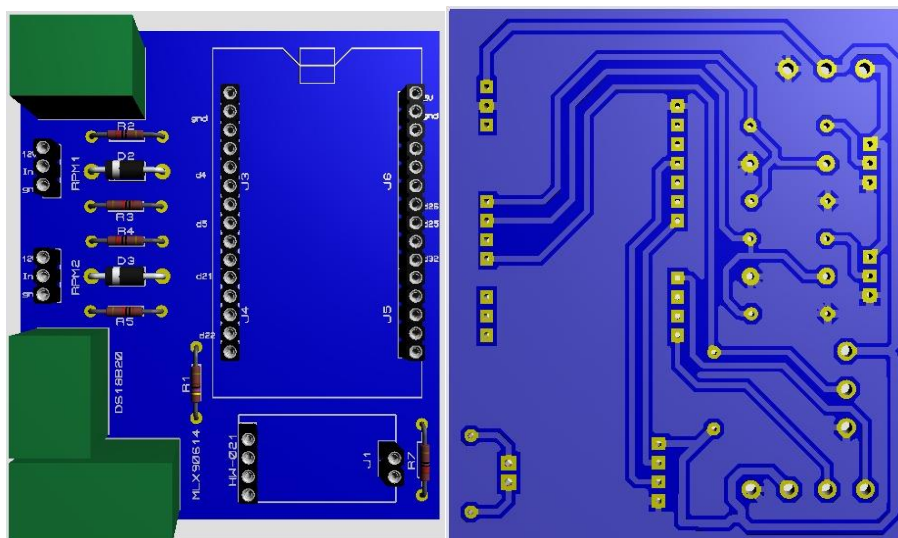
PCB ECU Sensores (Próprio Autor, 2021)
